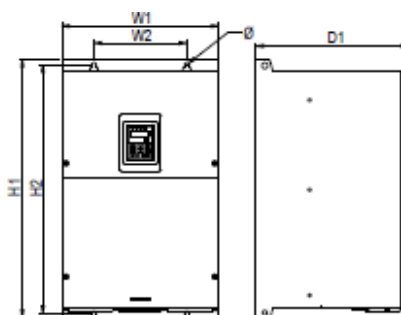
Настенный монтаж 75 – 110 кВт
